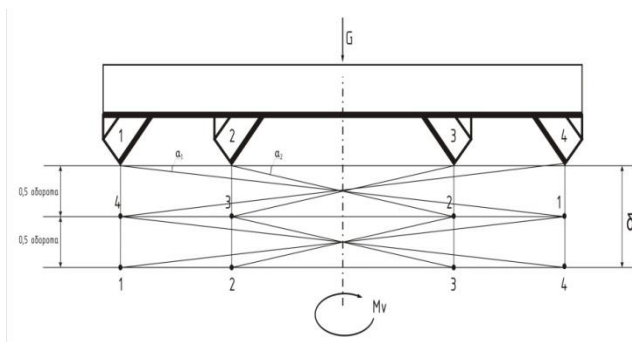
Схема перемещения резцов долота PDC: 1-4 – резцы типа Stratapax™, закрепленные в корпусе долота; G – осевая нагрузка на долото; M_v – крутящий момент на долоте; δ – углубка инструмента за оборот; α_i – углы наклона траектории заглубления резцов
